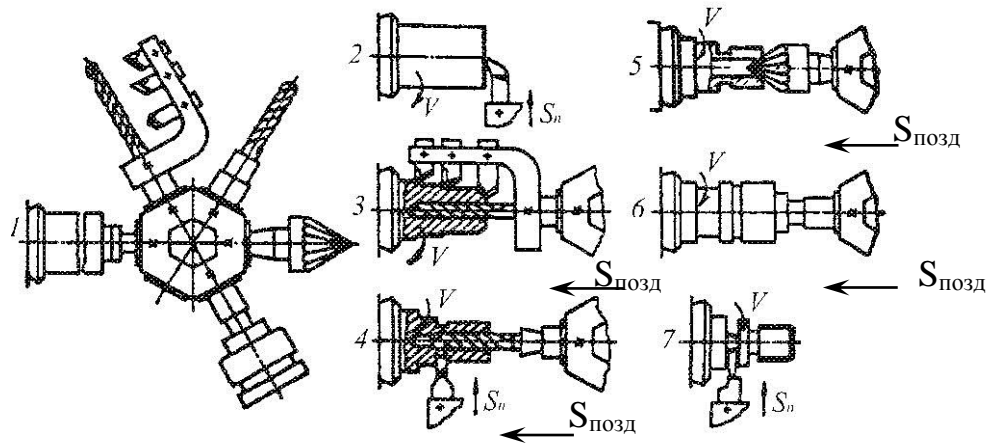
Схеми обробки поверхонь заготовок на токарно-револьверних верстатах
